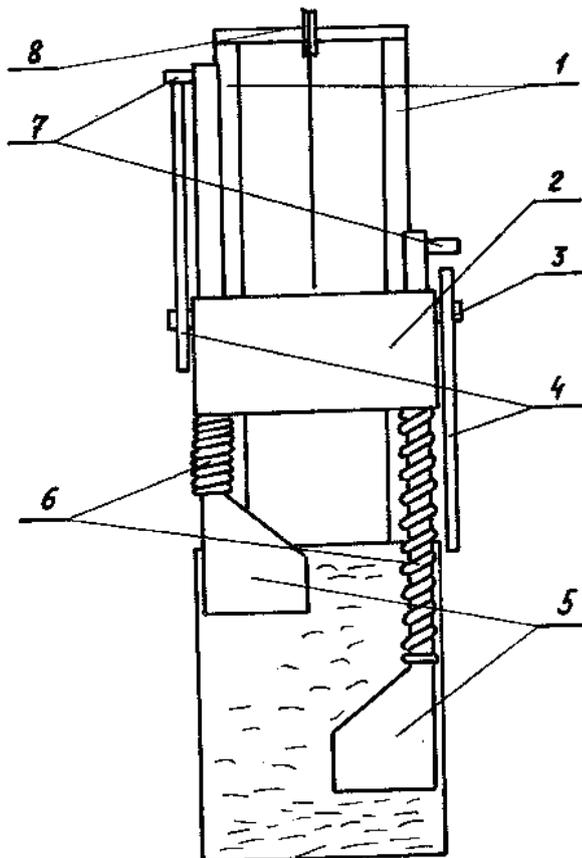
Схема уплотнителя травяной массы в контейнере: 1 – опора; 2 – приводной механизм; 3 – кулачки; 4 – вал; 5 – уплотняющие грузы; 6 – пружины; 7 – пальцы; 8 – подъемный механизм
